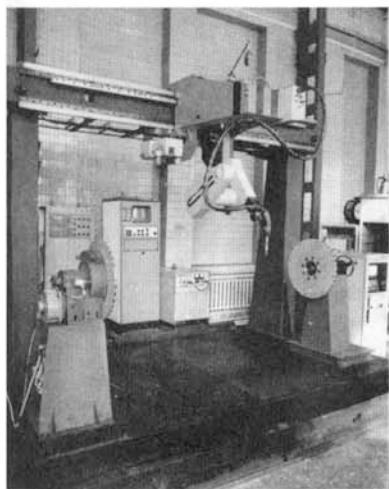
РТК с вращателем изделия для дуговой сварки конструкций средних габаритных размеров
